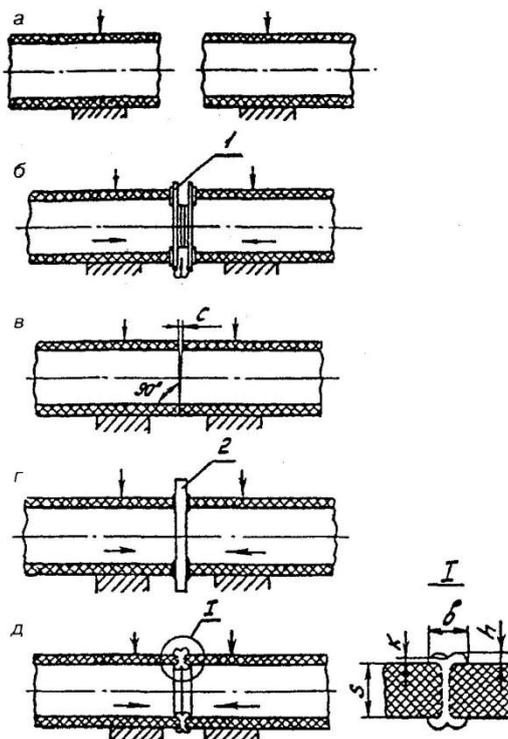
Этапы стыковой сварки труб:
